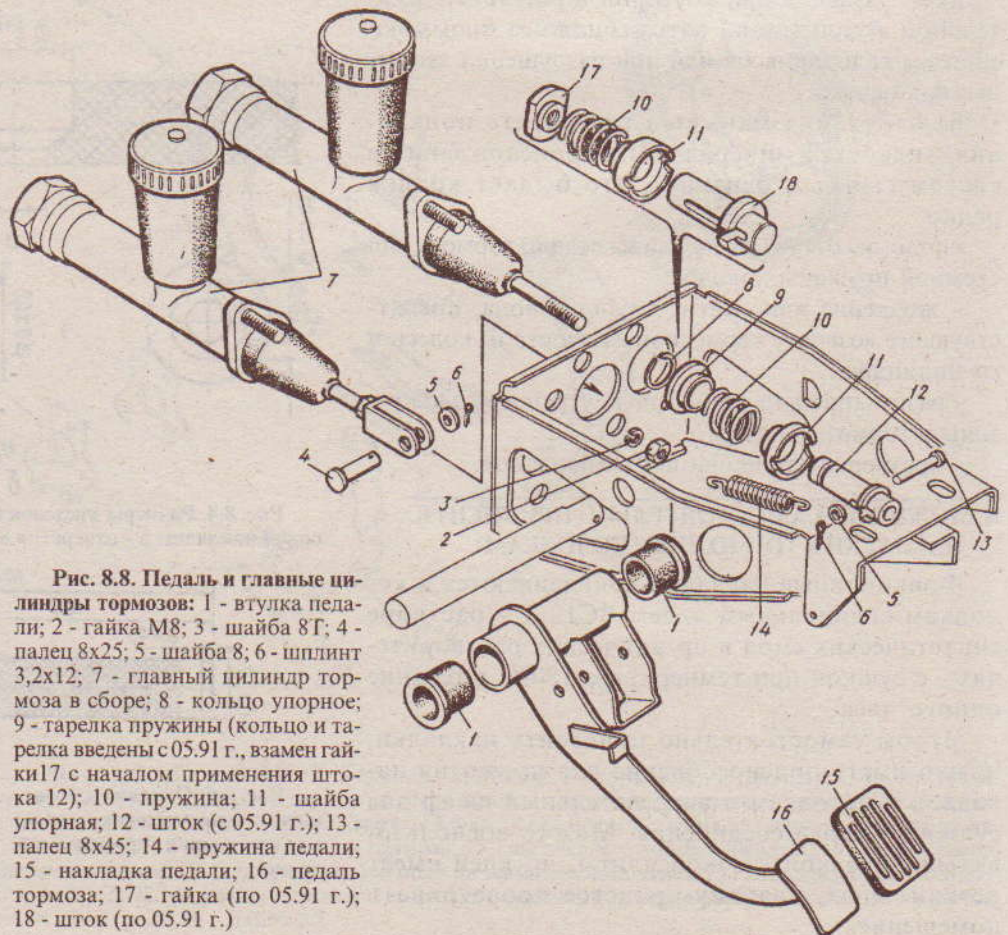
Педаль и главные цилиндры тормозов: 1 - втулка педали; 2 - гайка М8; 3 - шайба 8Г; 4 - палец 8x25; 5 - шайба 8; 6 - шплинт 3,2x12; 7 - главный цилиндр тормоза в сборе; 8 - кольцо упорное; 9 - тарелка пружины (кольцо и тарелка введены с 05.91 г., взамен гайки 17 с началом применения штока 12); 10 - пружина; 11 - шайба упорная; 12 - шток (с 05.91 г.); 13 - палец 8x45; 14 - пружина педали; 15 - накладка педали; 16 - педаль тормоза; 17 - гайка (по 05.91 г.); 18 - шток (по 05.91 г.)
